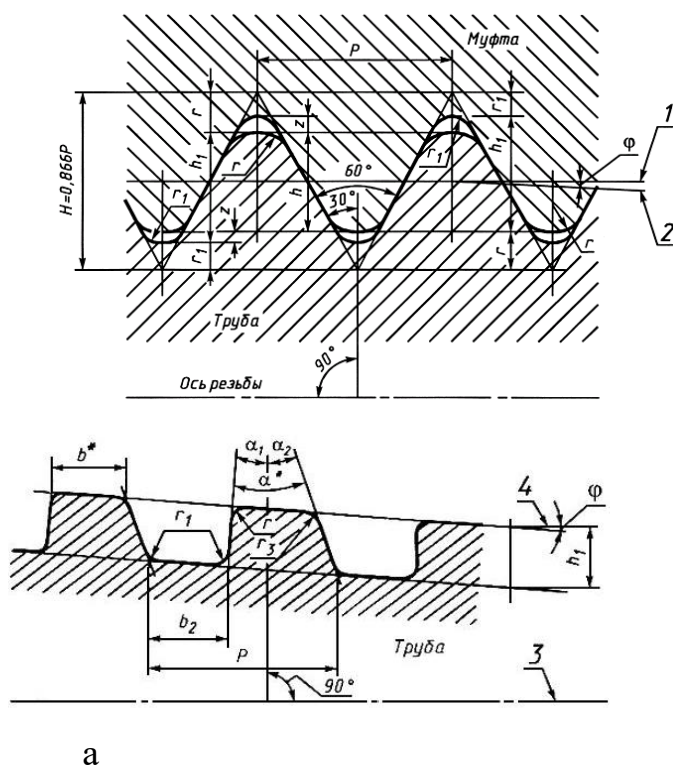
Профили резьб НКТ 73 (а) и упорной резьбы Buttress (б)
